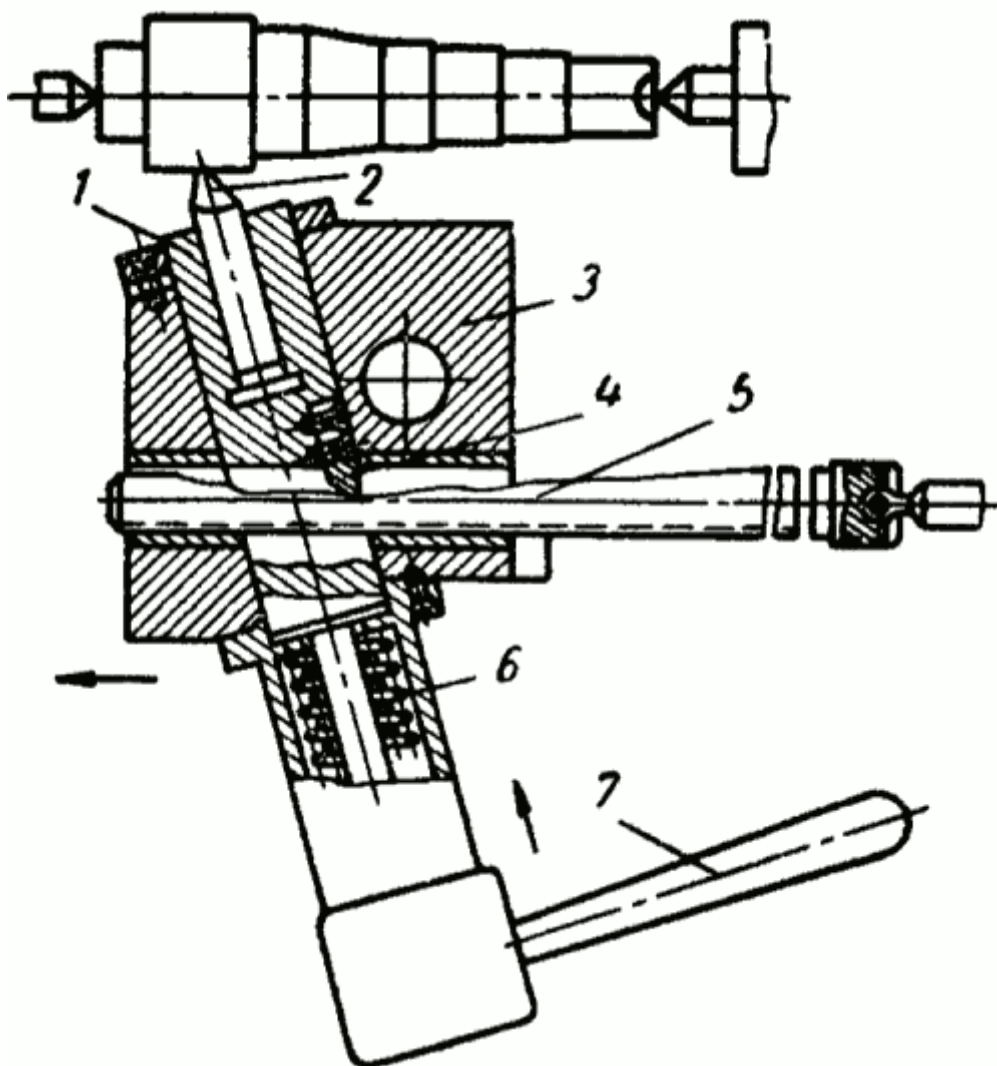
Копировальное приспособление конструкции В.К. Семинского для токарного станка
